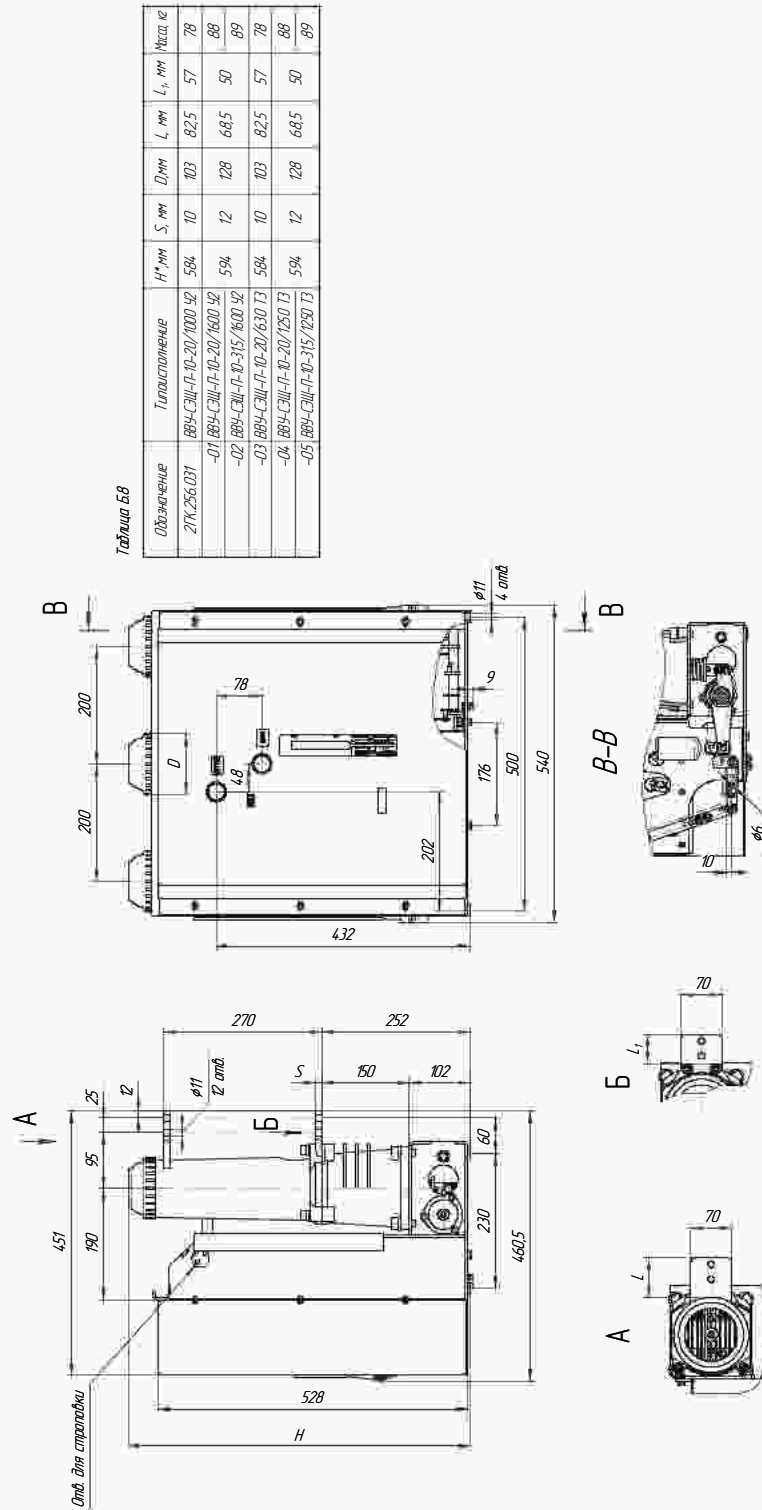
Габаритные, присоединительные и установочные размеры выключателя типа ВВУ-СЭЦ-П-10-20(31,5)/η (СЭЦ-70)
